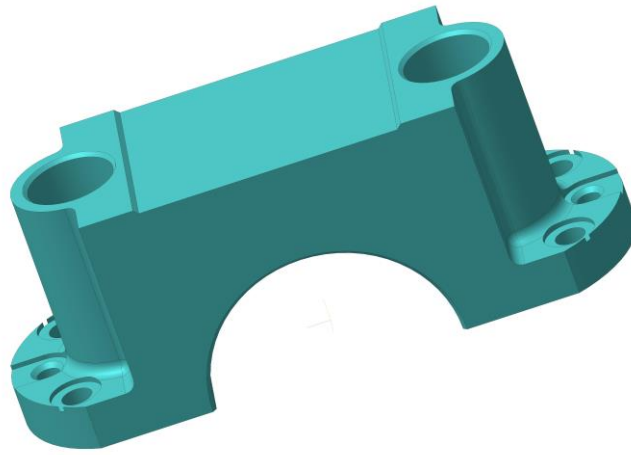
D модель корпусу змодельована в SolidWorks
